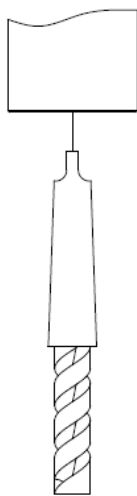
| Beispiel für die Befestigung eines Bohrers mit einem Schlüssel]
